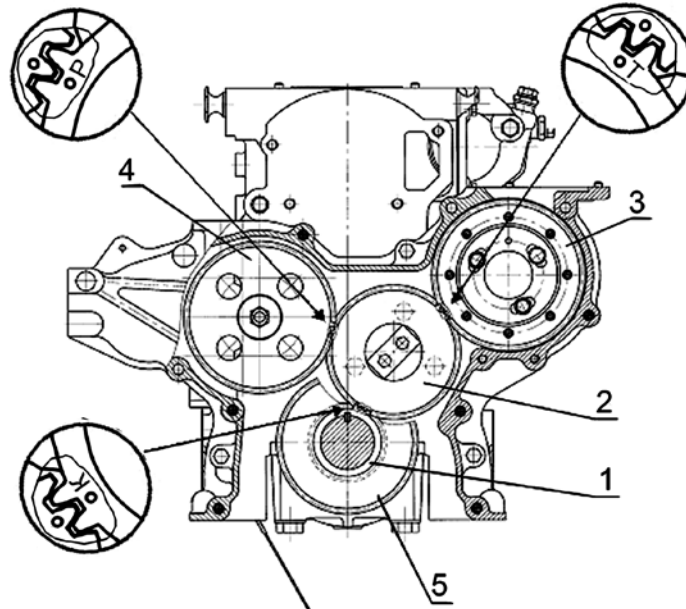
Схема установки шестерен распределения. 1 – шестерня коленчатого вала; 2 – промежуточная шестерня; 3 – шестерня привода топливного насоса; 4 – шестерня распределительного вала; 5 – шестерня привода масляного насоса.
